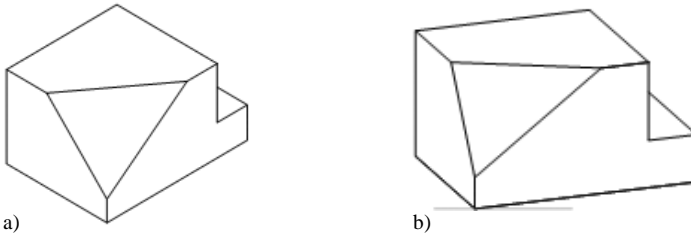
Projecções axonométricas: a) Isométrica; b) Dimétrica.
